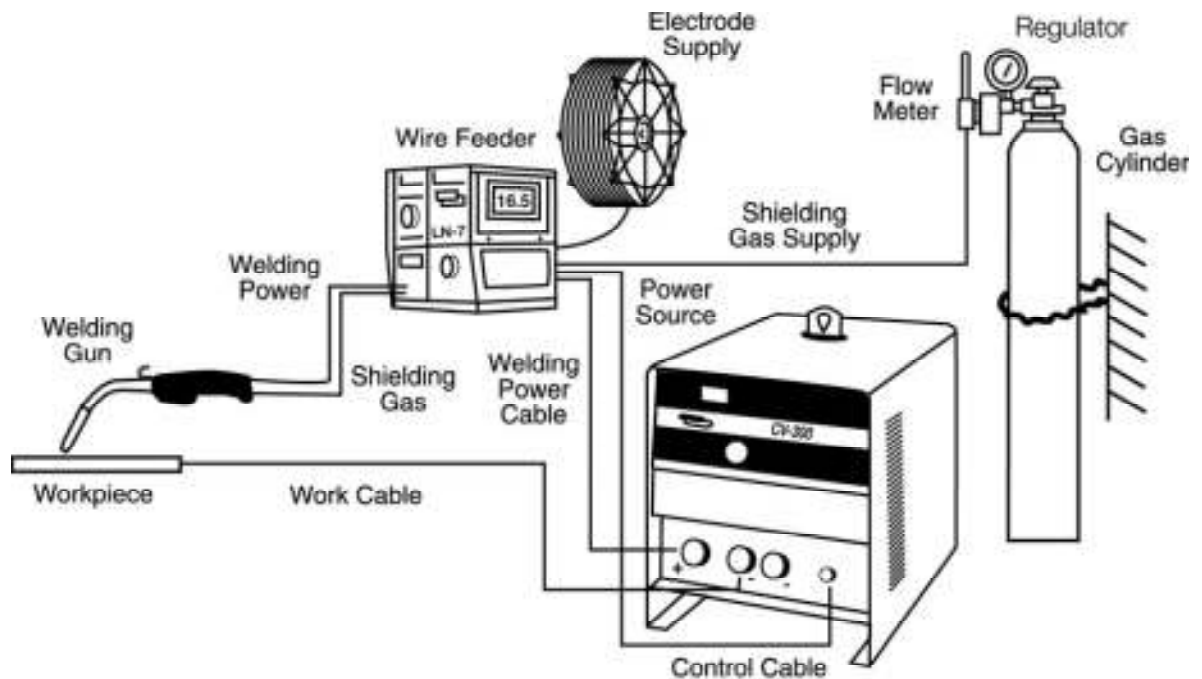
Componentes del Equipo de GMAW. Lincoln Soldaduras de Colombia, presentación (2007). p. 8
